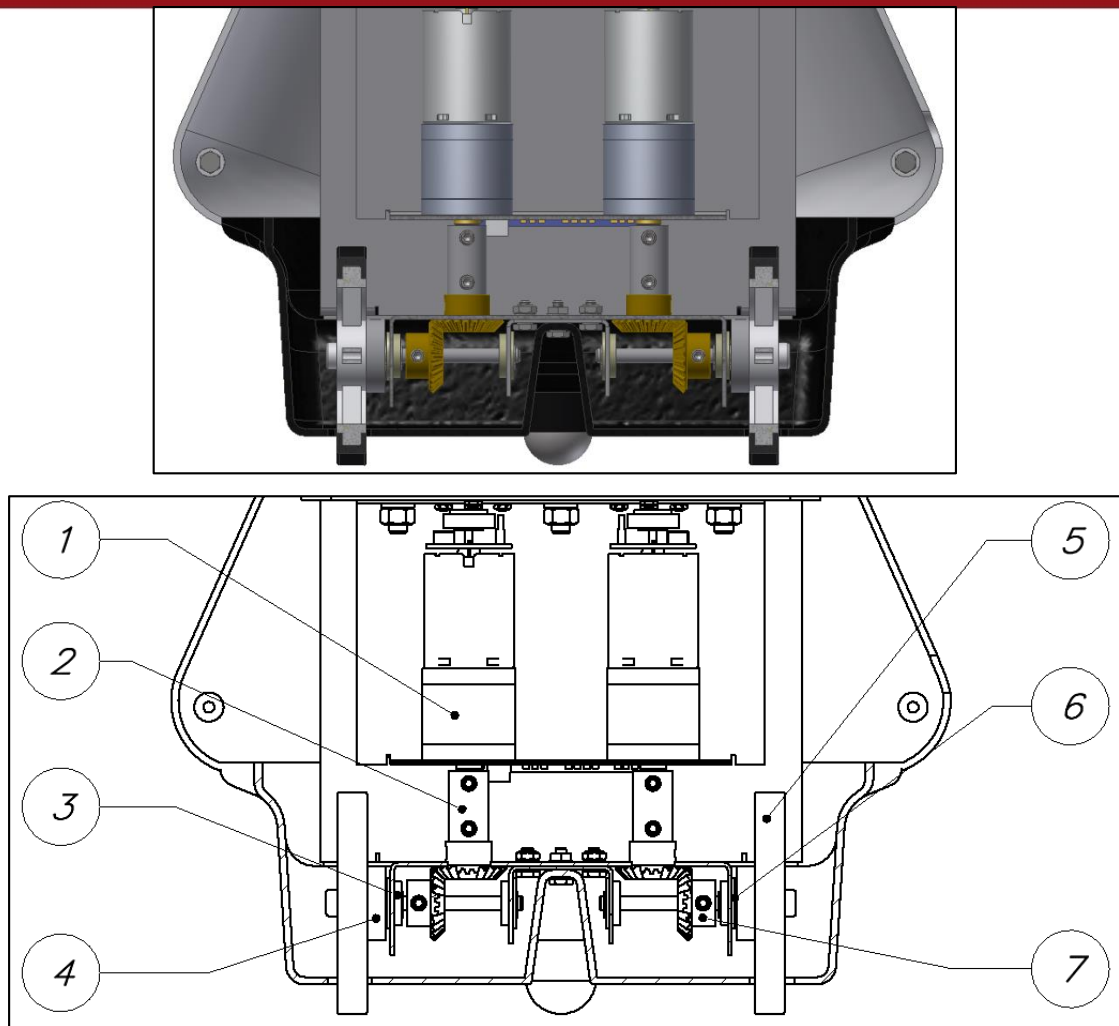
Vistas frontales de corte de MUQUI con la transmisión de engranajes cónicos visible
